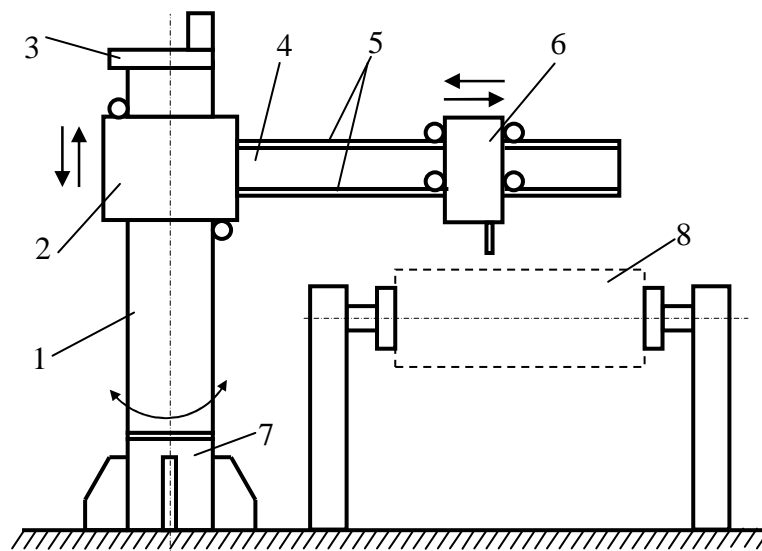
Підйомно-поворотна колонна для самохідних зварювальних апаратів: 1 – стояк поворотний; 2 – каретка; 3 – привод піднімання і опускання каретки; 4 – консоль; 5 – напрямні для зварювального апарату; 6 – самохідний зварювальний апарат; 7 – основа колони; 8 – обертач або кантувач;
